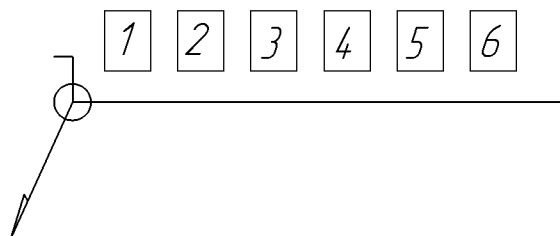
Схема условного обозначения сварного шва.
